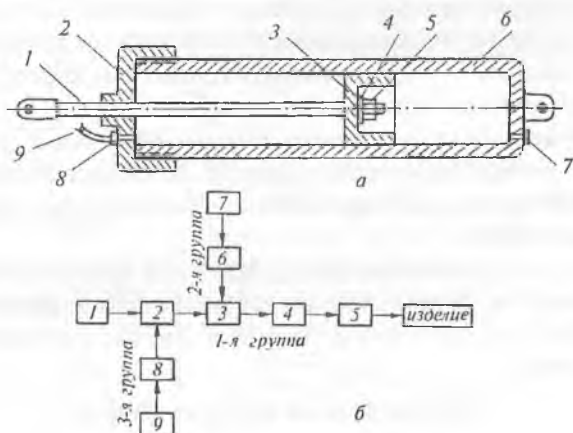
Сборка узла по базовой детали: а — эскиз цилиндра; б — схема сборки; 1 — шток; 2 — крышка; 3 — поршень; 4 — шайба; 5 — гайка; 6 — цилиндр; 7 и 8 — штуцер; 9 — шланг
